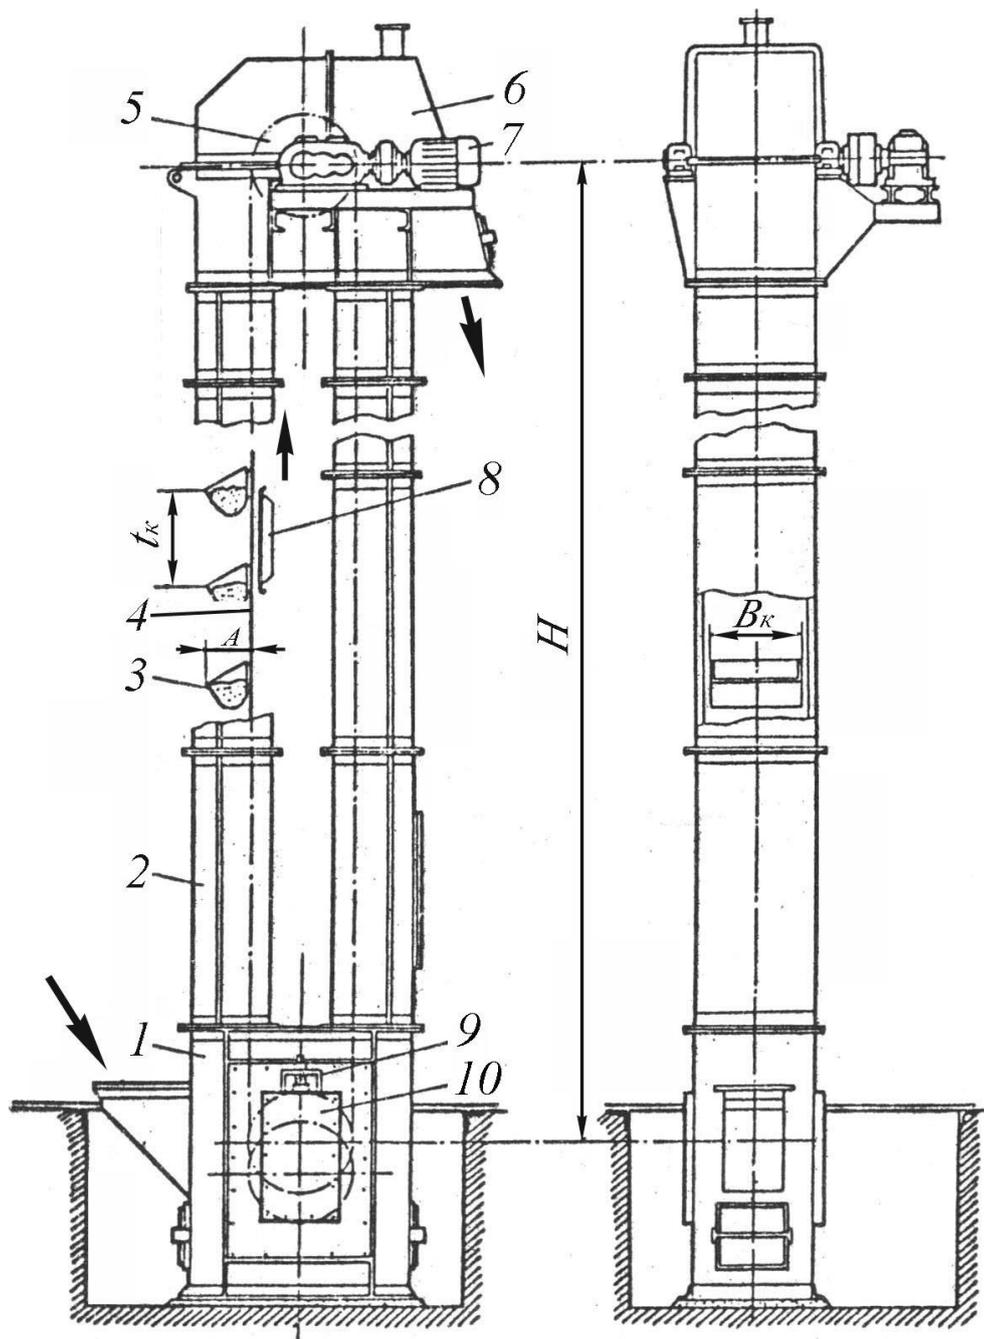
Вертикальный ленточный ковшовый элеватор.
